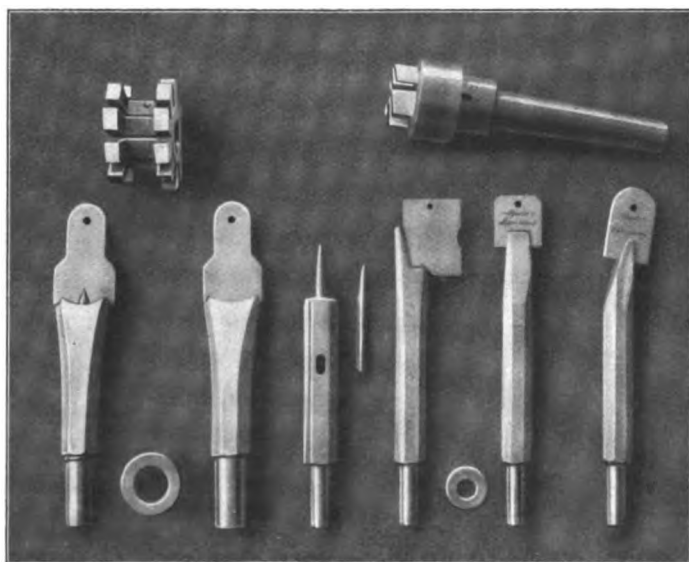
Lehren und Fräser für Kesselwerkzeuge.
